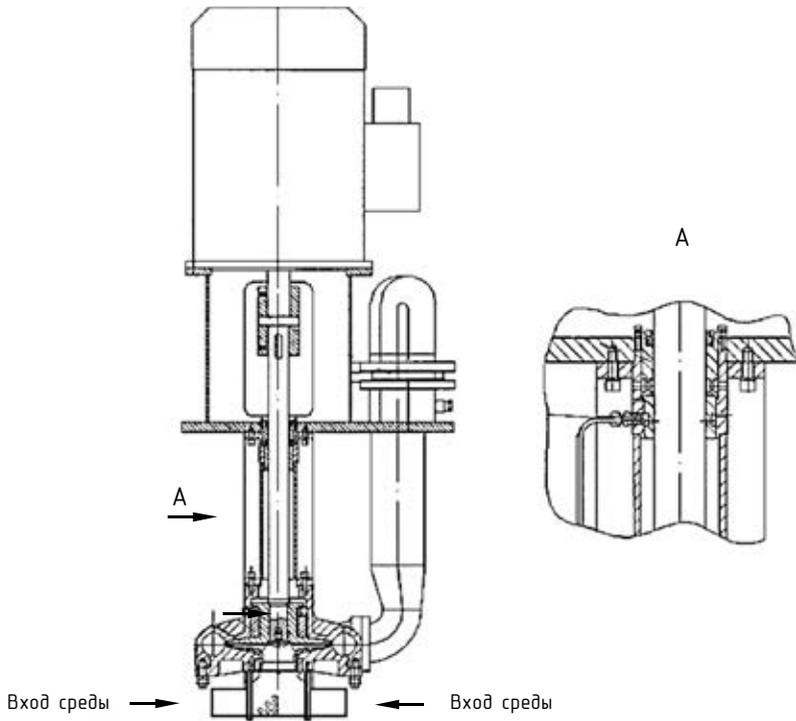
Конструкция ВМН со смазкой подшипников охлаждающего воздуха
